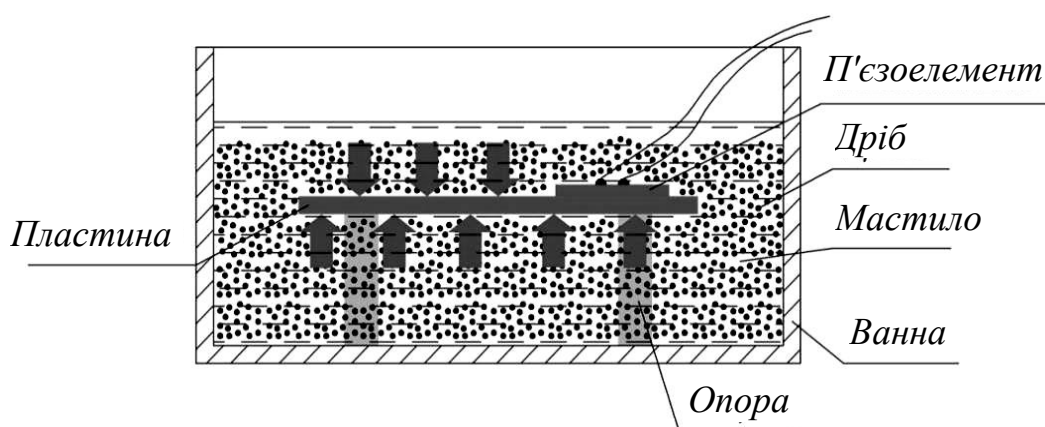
Схема установки пластины в пружном середовищі при віброобробленні
